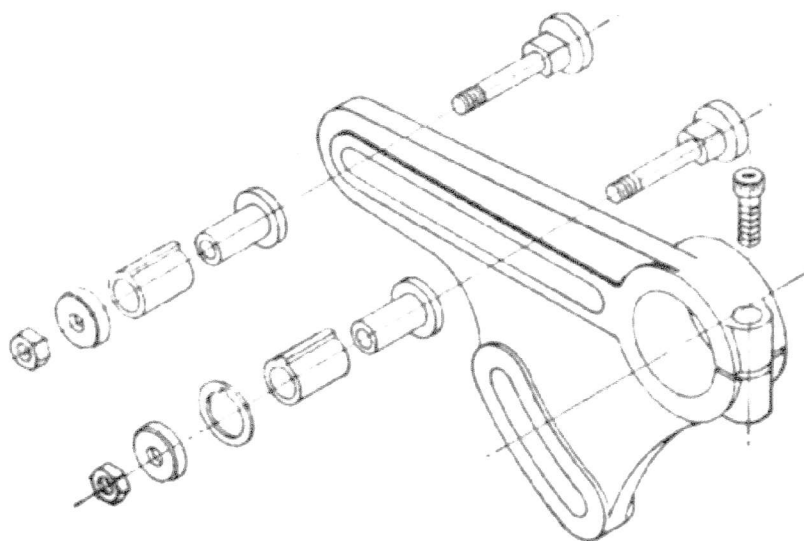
Lyre (vue "éclatée" présentant le montage des axes mobiles du train d'engrenages).
